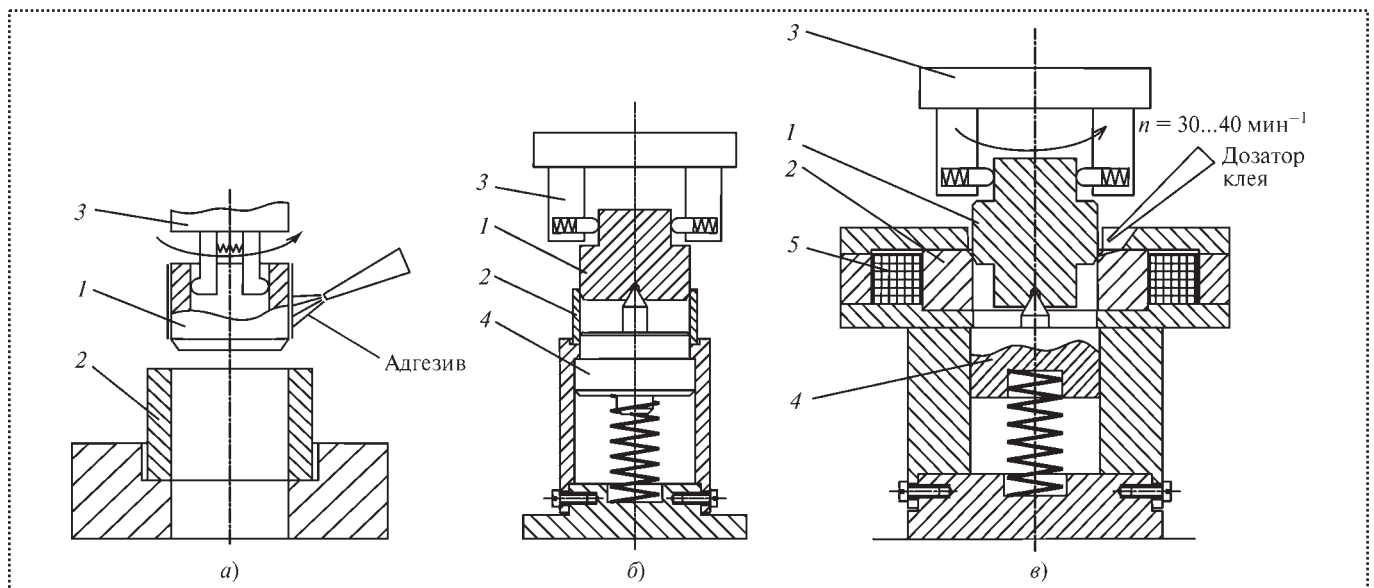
Схемы исполнительных механизмов для выполнения цилиндрических соединений с натягом клеевым методом: 1 – присоединяемая деталь; 2 – базовая деталь; 3 – схват робота; 4 – подпружиненный ловитель; 5 – индуктор
